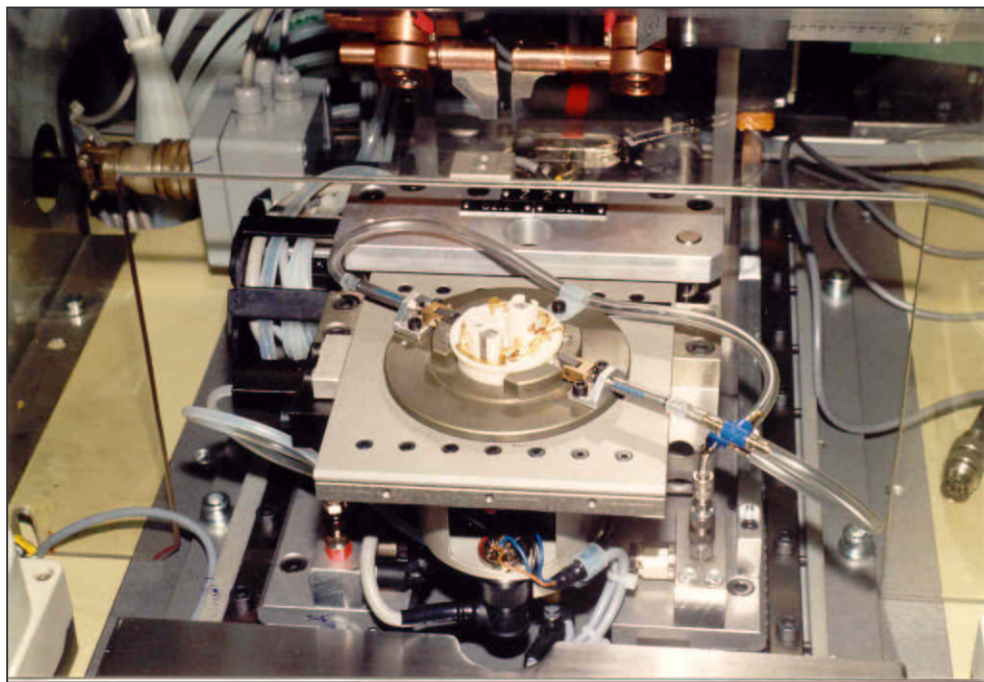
Schweißvorrichtung zum Widerstandschweißen von elektrischen Verbindungen. Da eine Elektrode fest ist und die zweite sich zur ersten hinbewegt, würde sich das Bauteil verbiegen. Da es aber in einem einachsigen TA liegt, erlaubt dieser das definierte Mitgehen des Bauteils, ohne daß es beschädigt wird. Ausgleichswege $+10\text{mm}$. Nach dem Schweißen bringt der Ta das Teil wieder passiv in seine Null-Lage.
